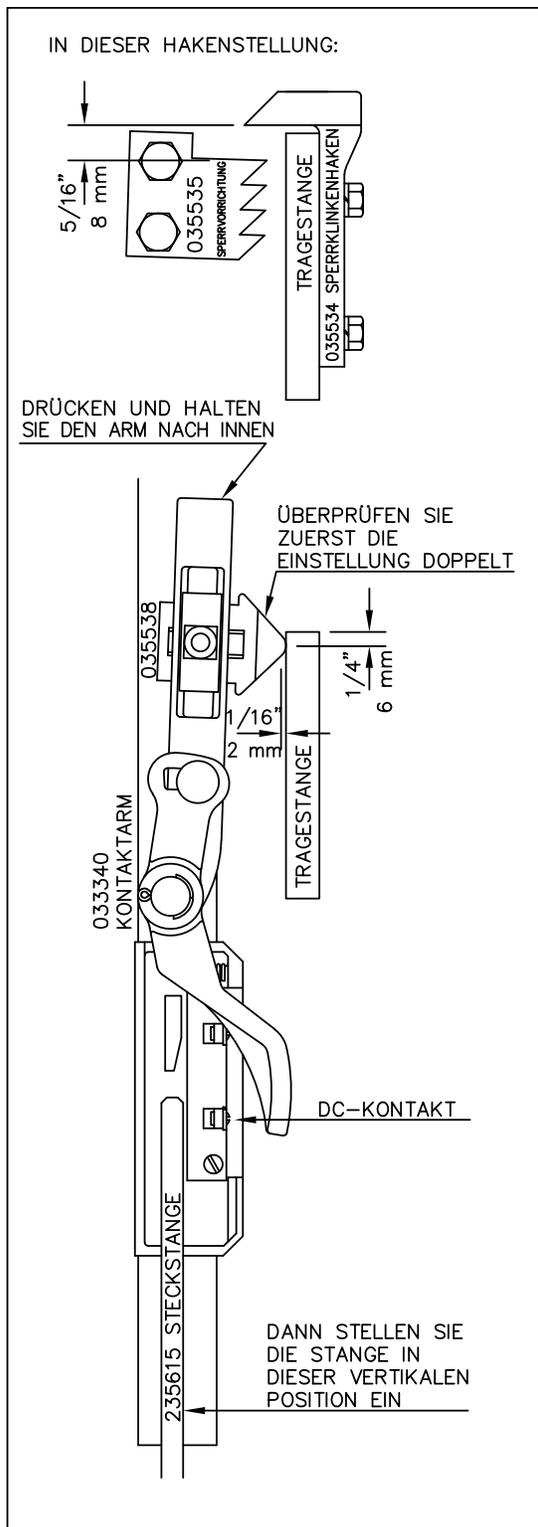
Einstellung des Steckgestänges geschlossen
